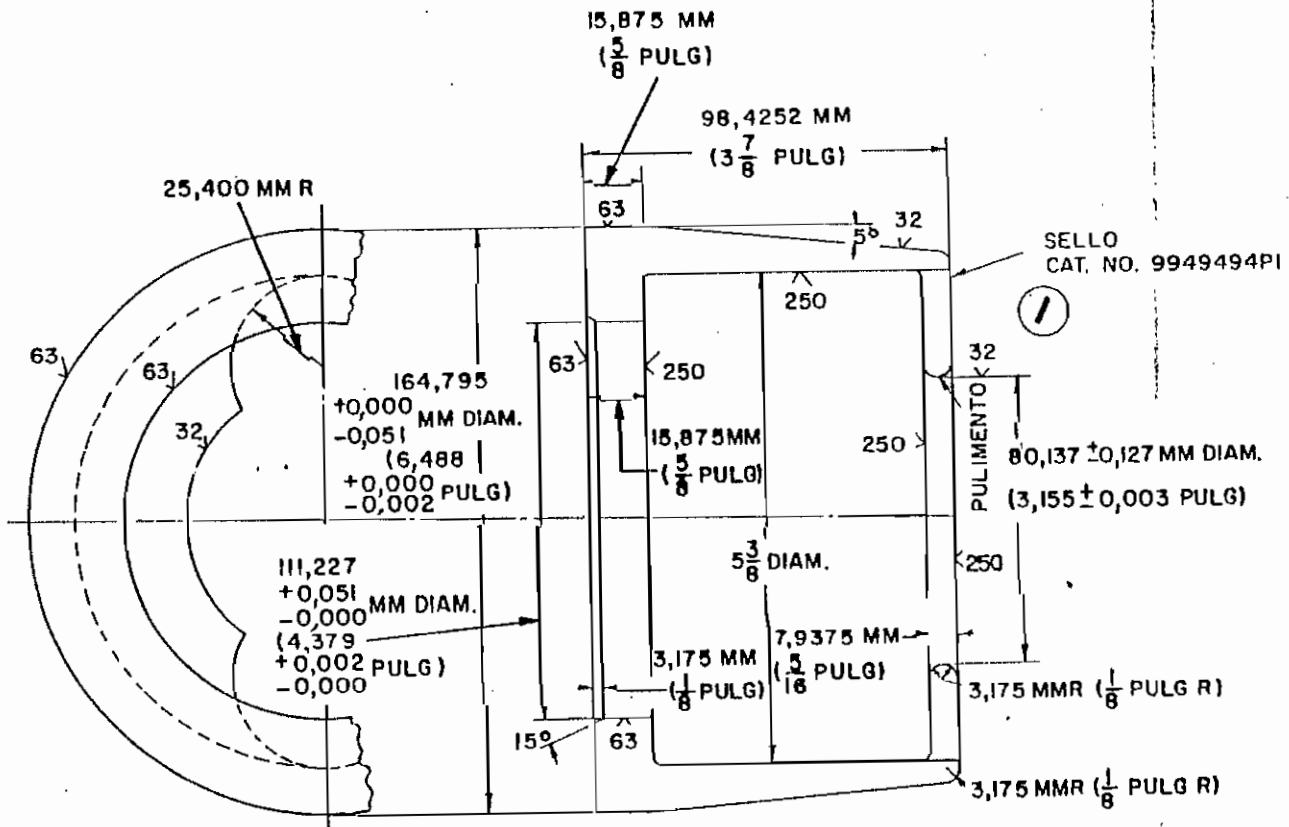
Guía del cojinete de rodillos (extremo del piñón)
